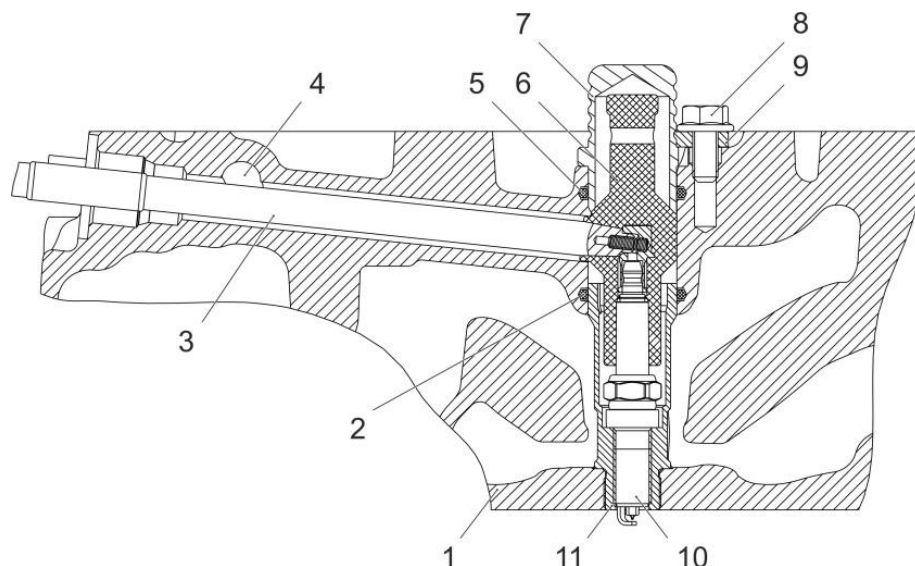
Установка свечи зажигания в головке цилиндров:
